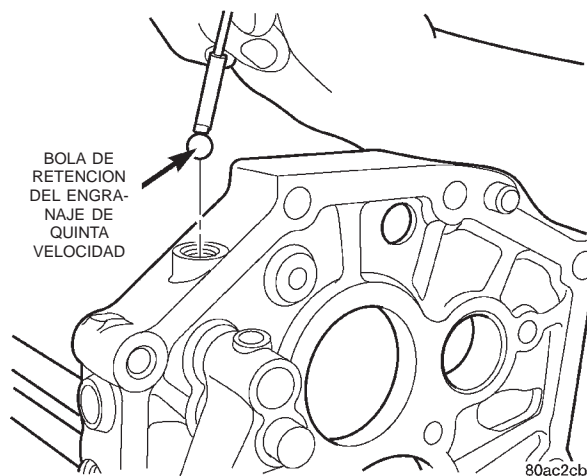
Desmontaje de bola de retención del engranaje de quinta velocidad
